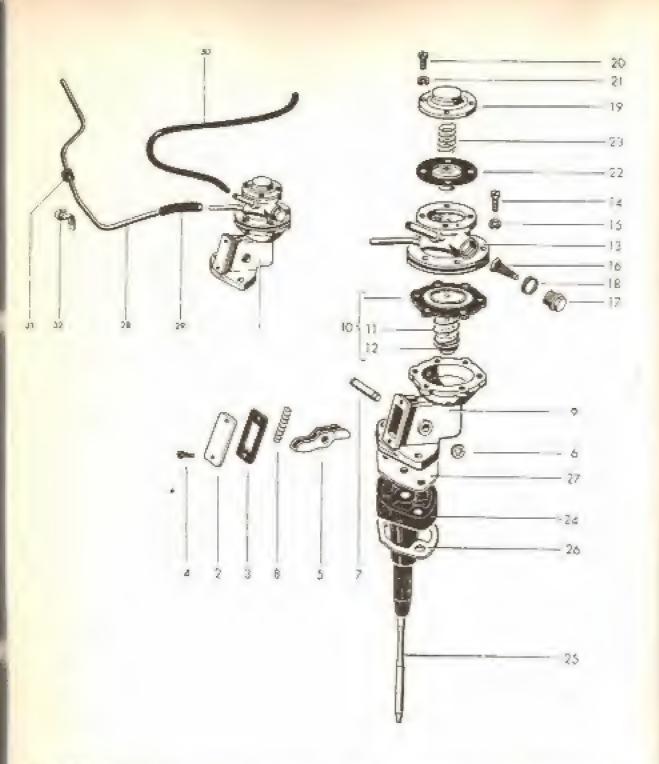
F. — Bomba de gasolína do sedan "1 360" montada (acima a esquerda) e desmontada, Peças principais: 5 — balancim; 7 — eixo do balancim; 8 — mola do balancim; 9 — corpo inferior da bomba; 10 — conjunto do diafragma; 13 — corpo superior da bomba; 16 — filtro de tela; 17 — bujão do filtro; 19 — tampa; 22 — válvula de diafragma; 24 — flange de plástico; 25 — pino ou haste de comando; 27 e 28 — juntas; 29 e 30 — tubos de plástico.
